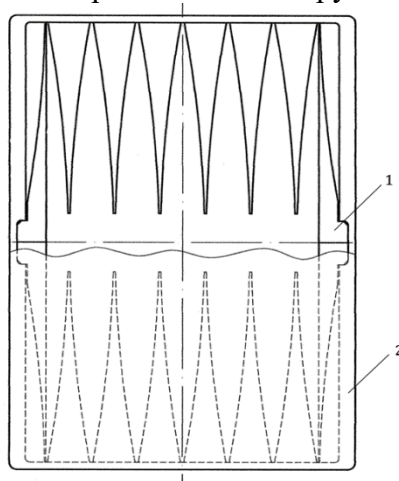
Конструкция фильтра, предложенная главным конструктором: 1 – полоски из металлического гафния, 2 – алюминиевая оболочка кассеты фильтра
